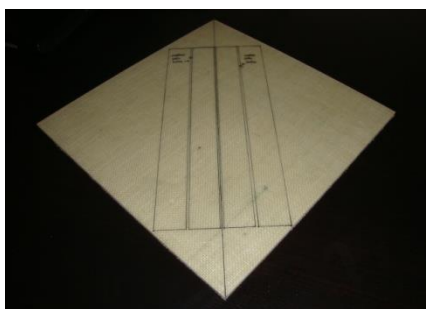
Placa de poliéster reforçado com tecido de juta, marcada com as dimensões dos provetes
